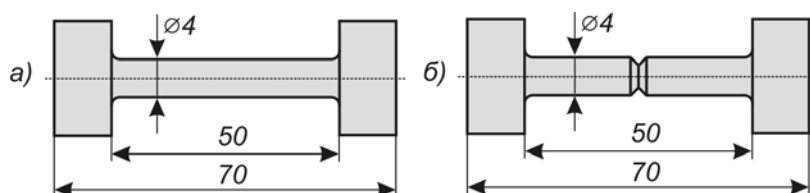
Образцы для испытаний: а – гладкий; б – с надрезом.
